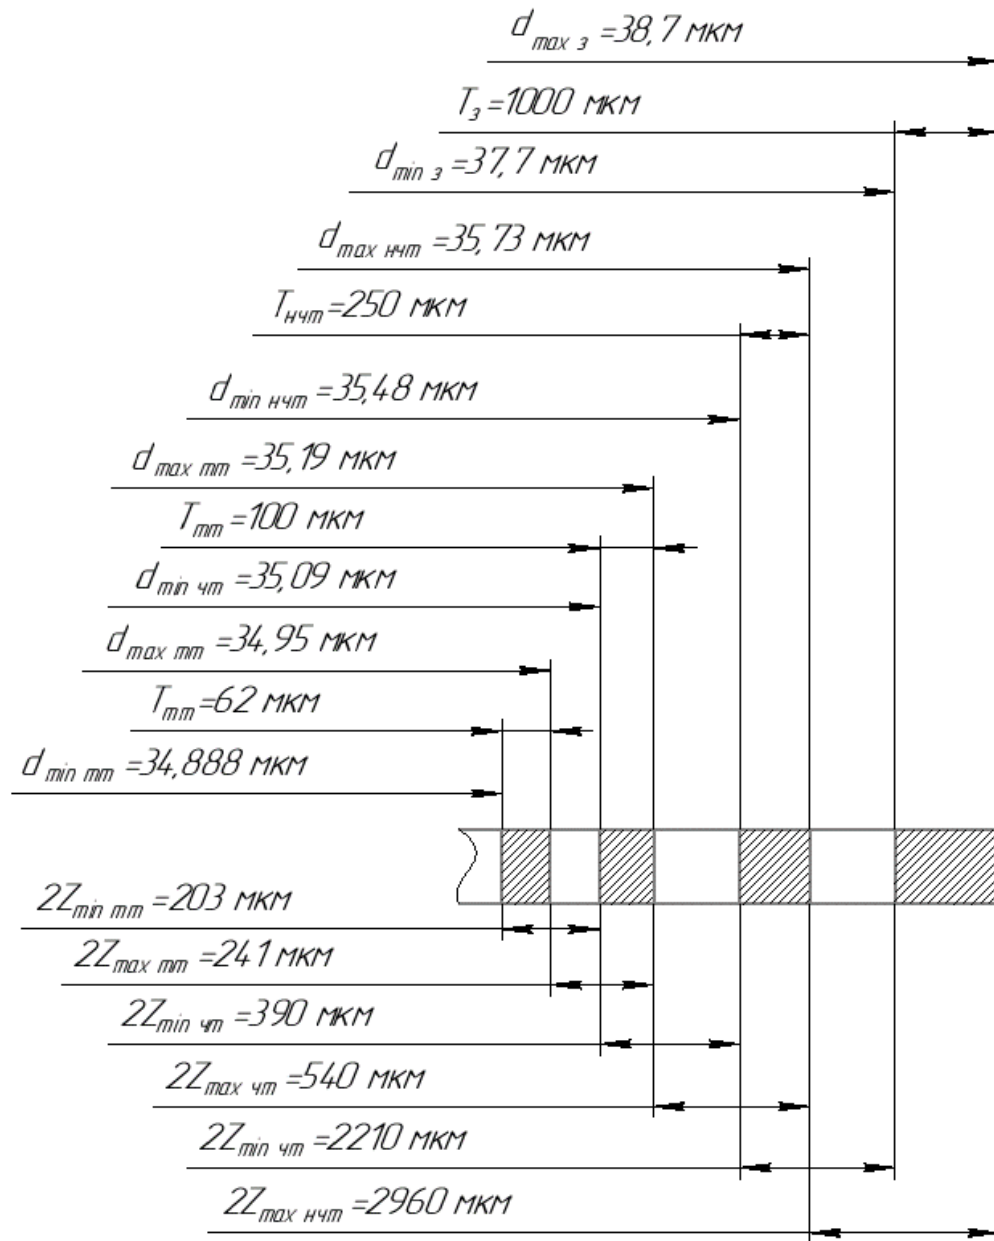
Схема графічного розташування припусків і допусків для обробки зовнішньої циліндричної поверхні $\varnothing 35 e9 \begin{pmatrix} -0.050 \\ -0.112 \end{pmatrix}$.
